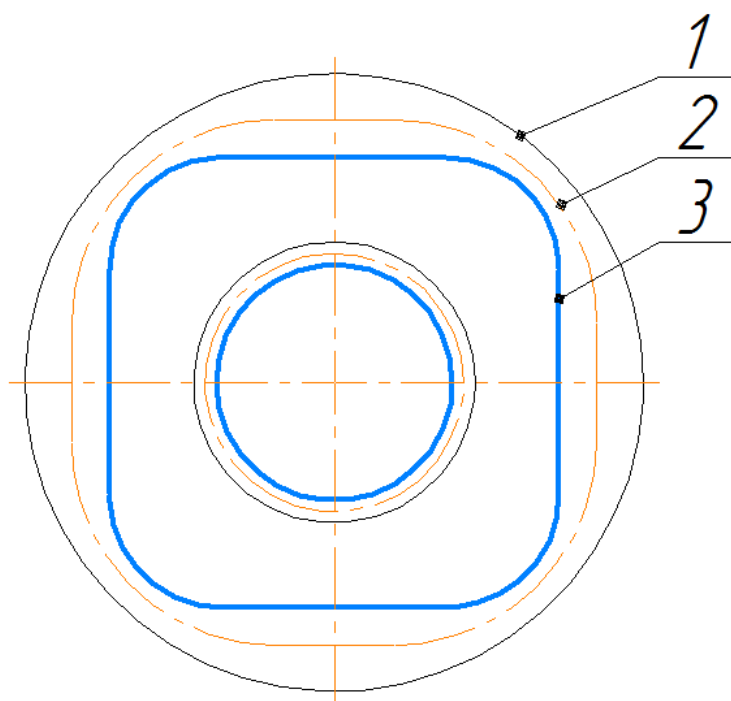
Двухпроходное волочение: круг – наружный квадрат. 1- контур заготовки, 2 - контур промежуточного перехода, 3 – готовая труба.
